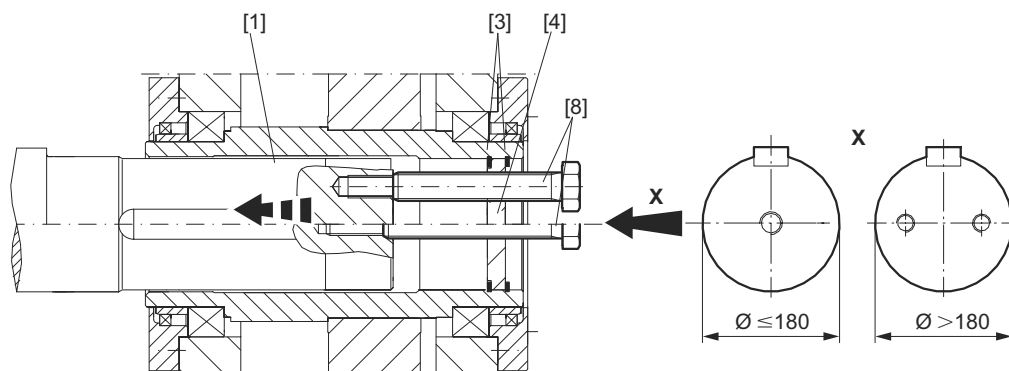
Demontage Horizontalgetriebe mit Passfederverbindung
